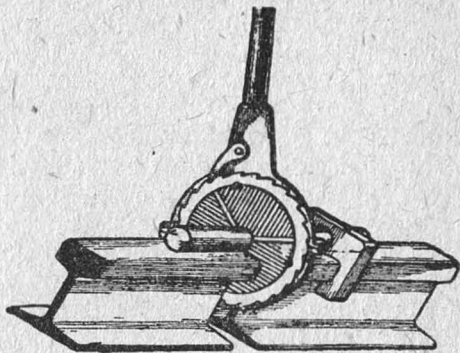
Термитная сварка рельсовых стыков.
